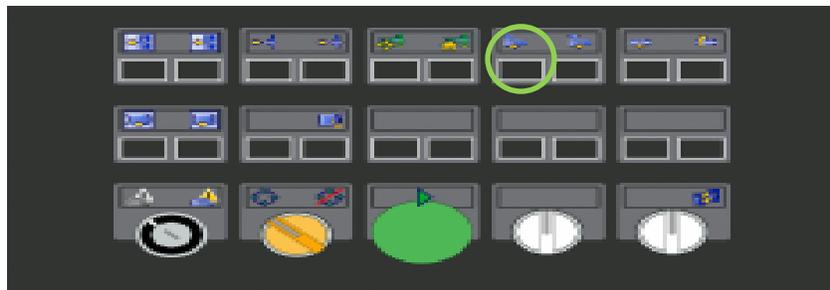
(operator manual machine duo 7050/1900 WP US ENGEL, 2013)
